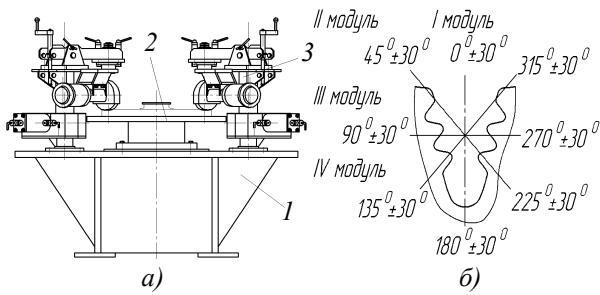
Схема агрегатного четырехмодульного станка (а) и направления обработки кромок торцевых поверхностей елочного паза диска турбины шлифовальными головками с полимерноабразивными щетками (б)
